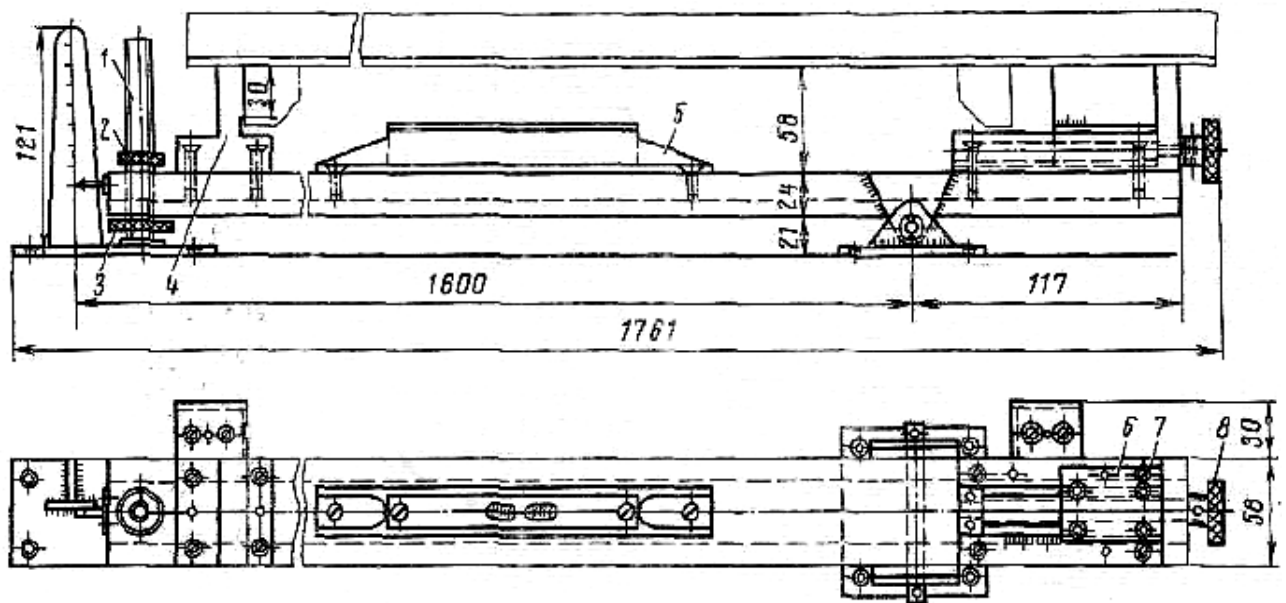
Стенд для перевірки колійних шаблонів: 1 – рухома опора; 2 – рівень; 3 – шарнірна опора; 4 – робочий шаблон, що встановлений на перевірку; 5 – рівень; 6 – гайка з конусом; 7 – опора права; 8 – головка гвинта.
